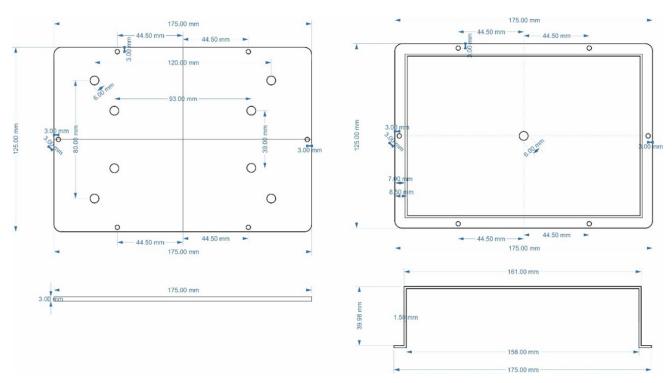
Чертеж корпуса блока БРЭСКА (дно и крышка)
